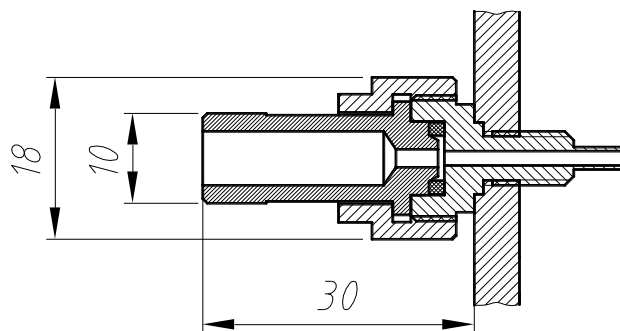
конструкция и размеры ниппеля для приварки к трубопроводу
